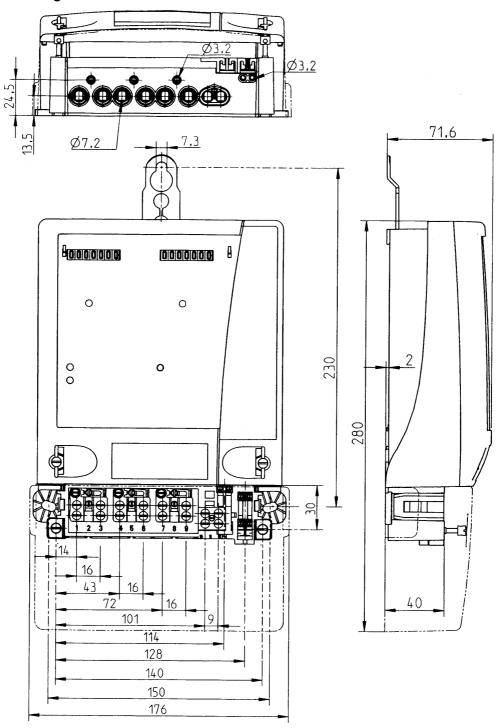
Hauptabmessungen und Klemmenblock für Zähler bis 85 A
